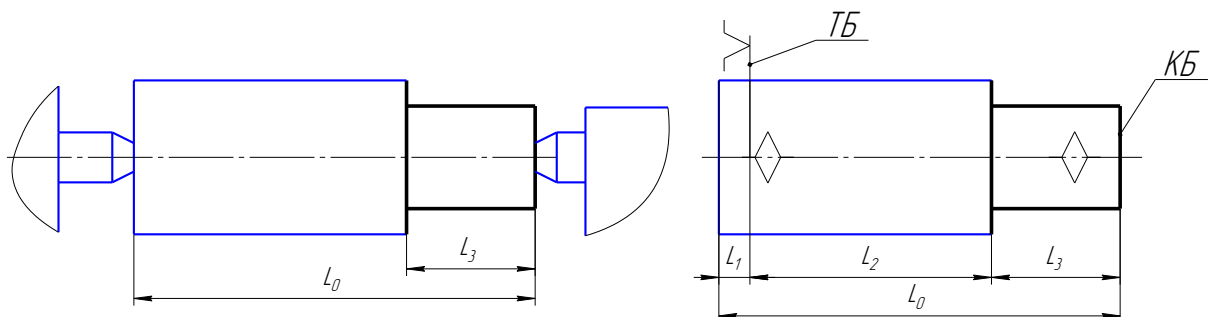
Розмірна схема операції обробки шийки вала для визначення похибки базування
